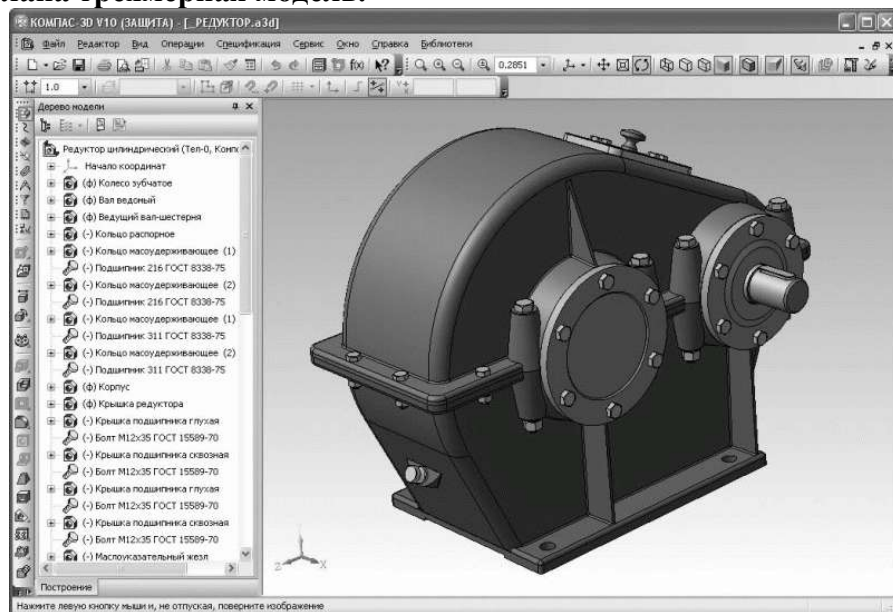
3D-модель цилиндрического одноступенчатого редуктора
